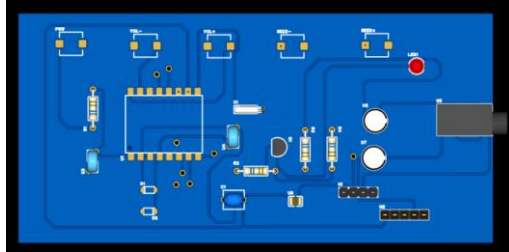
Tampilan 2D PCB (Bottom Side)
